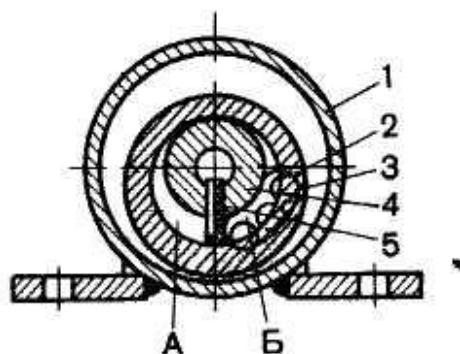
Вибровозбудитель пневматического прикрепляемого вибратора
